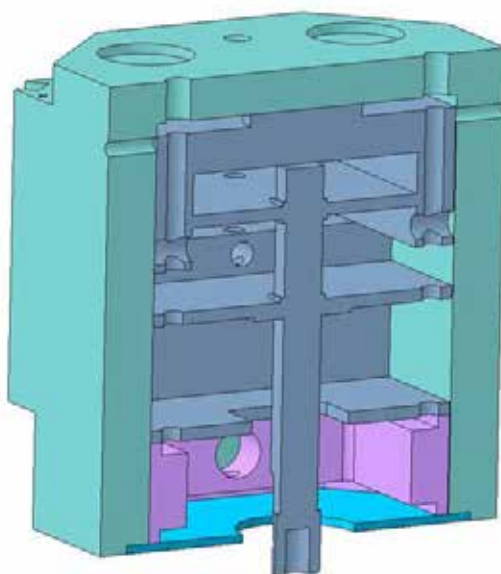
Силовосчувствительный элемент внутри подвижного корпуса
